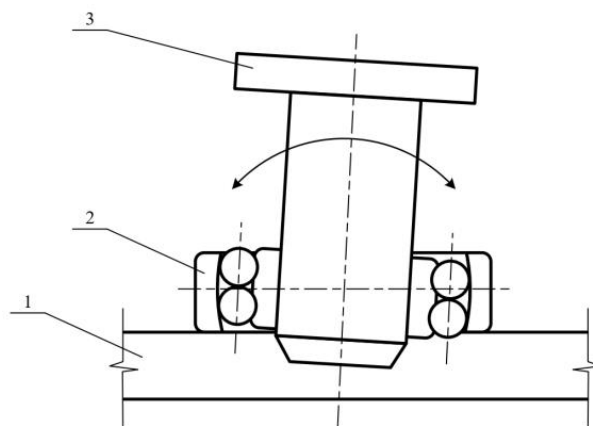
Подвижное основание устройства нагружающего, где 1) корпус; 2) самоцентрирующийся (самоустанавливающийся) шариковый подшипник; 3) столик-вставка
